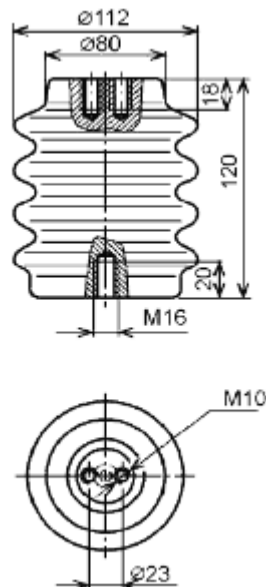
Размеры, внешний вид опорного изолятора ИОР-10-7.5 II УХЛ2
